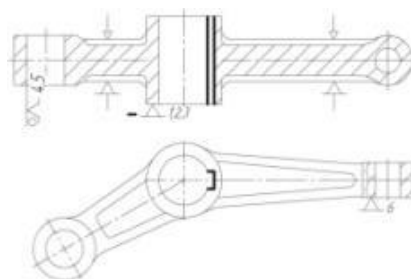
Схема базування заготовки на довбальній 35 операції
